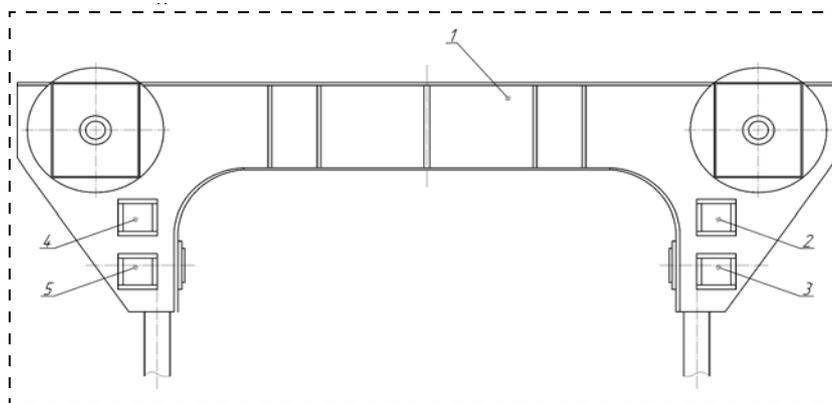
Места расположения образцов-"свидетелей" на траверсе литейного крана: 1 — траверса; 2 — образец № 2; 3 — образец № 1; 4 — образец № 4; 5 — образец № 3
